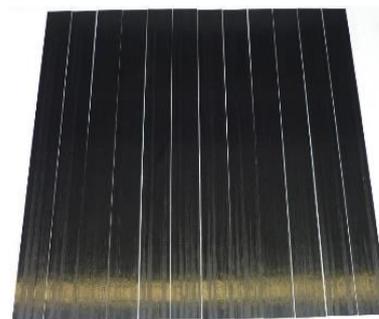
Gefertigte Prüfplattengeometrie (300x300mm)
